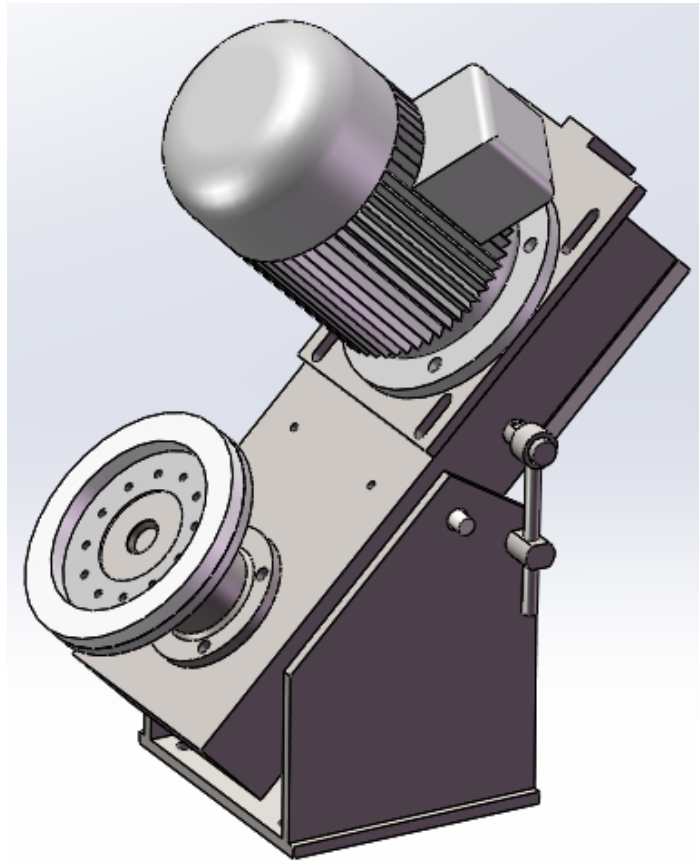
下倒角磨头 Figure 2-3 Lower chamfer head
